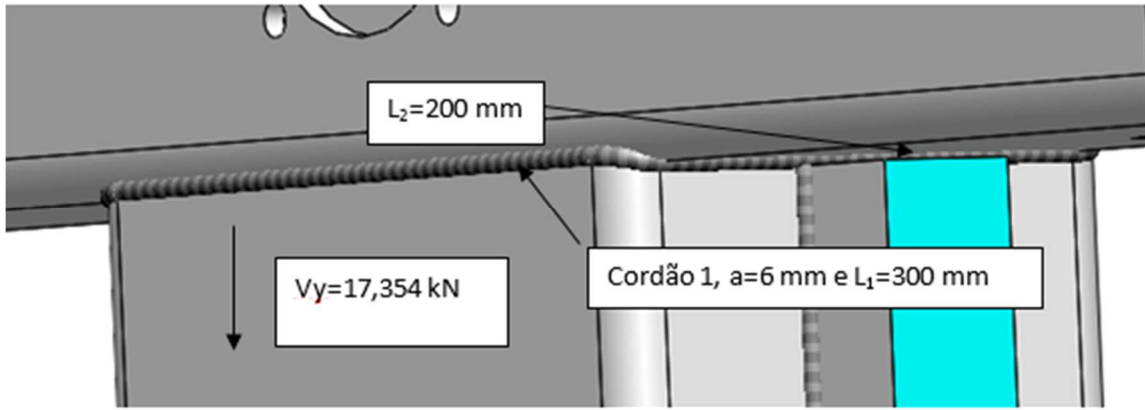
Ligação de soldadura com cordão de 6 mm.
